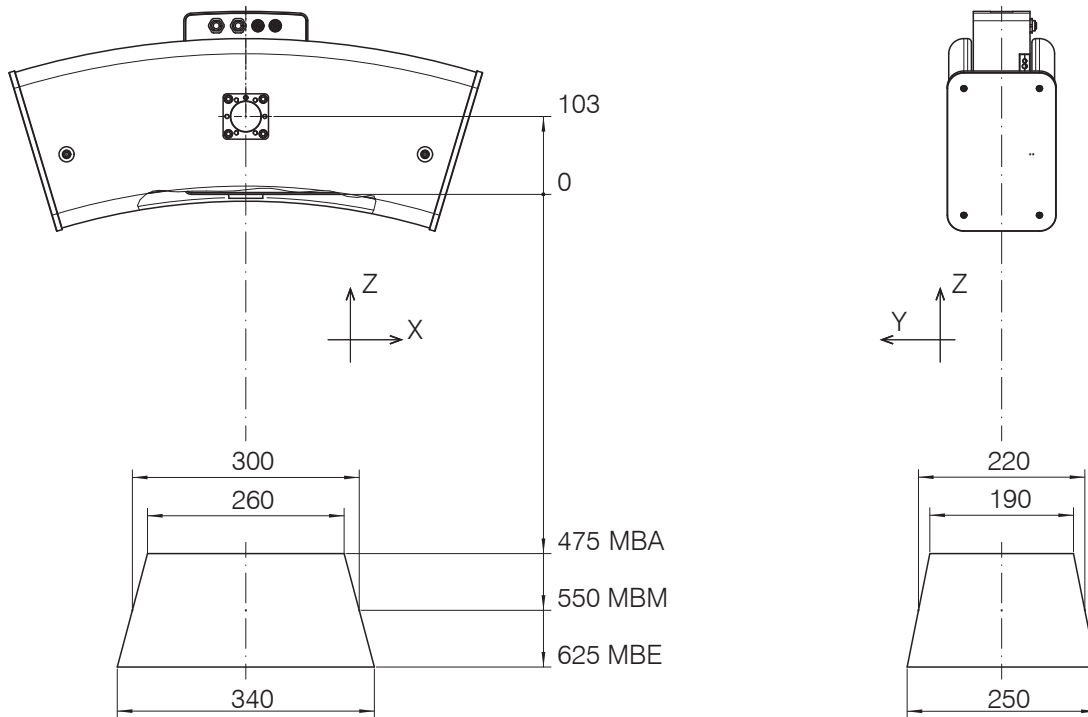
Maßzeichnung Messfeld surfaceCONTROL 3D SC25x0-300
